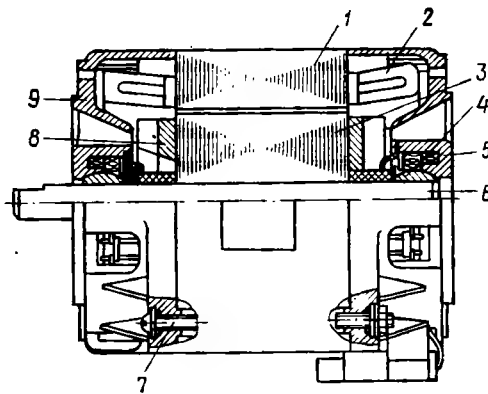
Конструкция конденсаторного асинхронного двигателя типа КДР:
